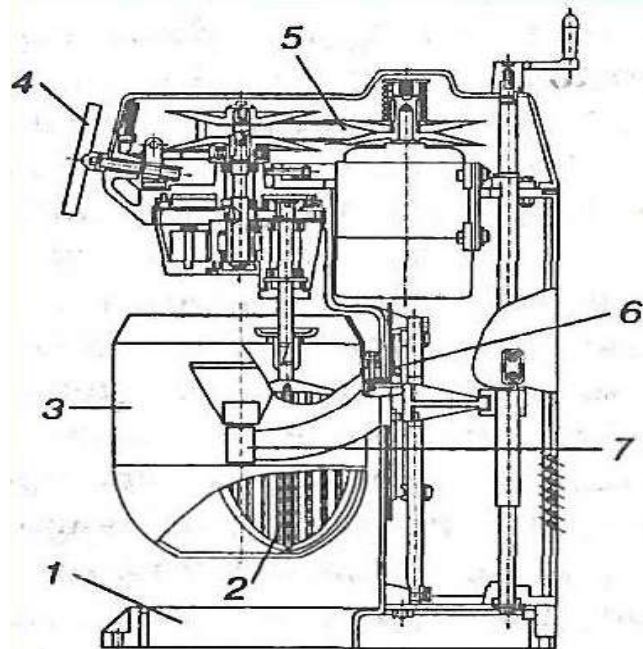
Збивальна машина МВ-35М: 1 – основа; 2 – збивачка; 3 – бачок; 4 – рукоятка коробки частоті обертів; 5 – варіатор; 6 – напрямна для переміщення бачка; 7 – кронштейн для бачка
